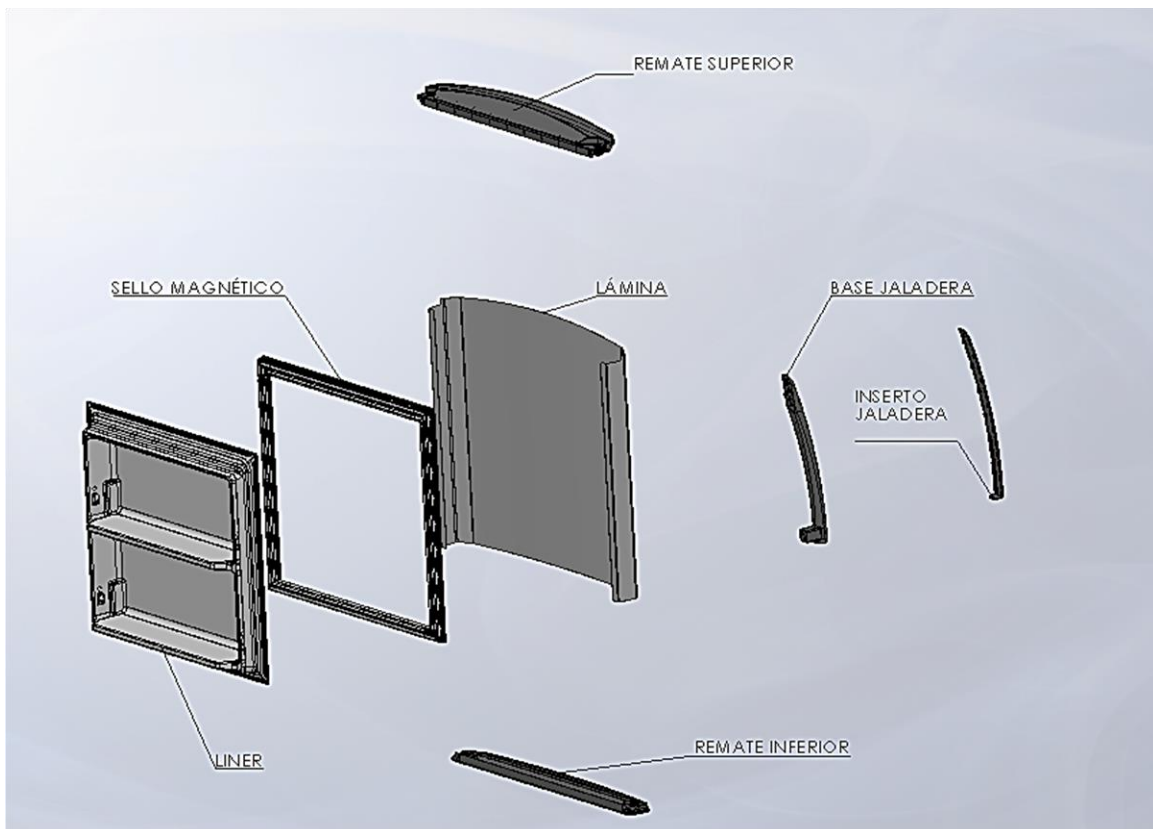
Vista explosionada del ensamble de la puerta del congelador (vista interior).
